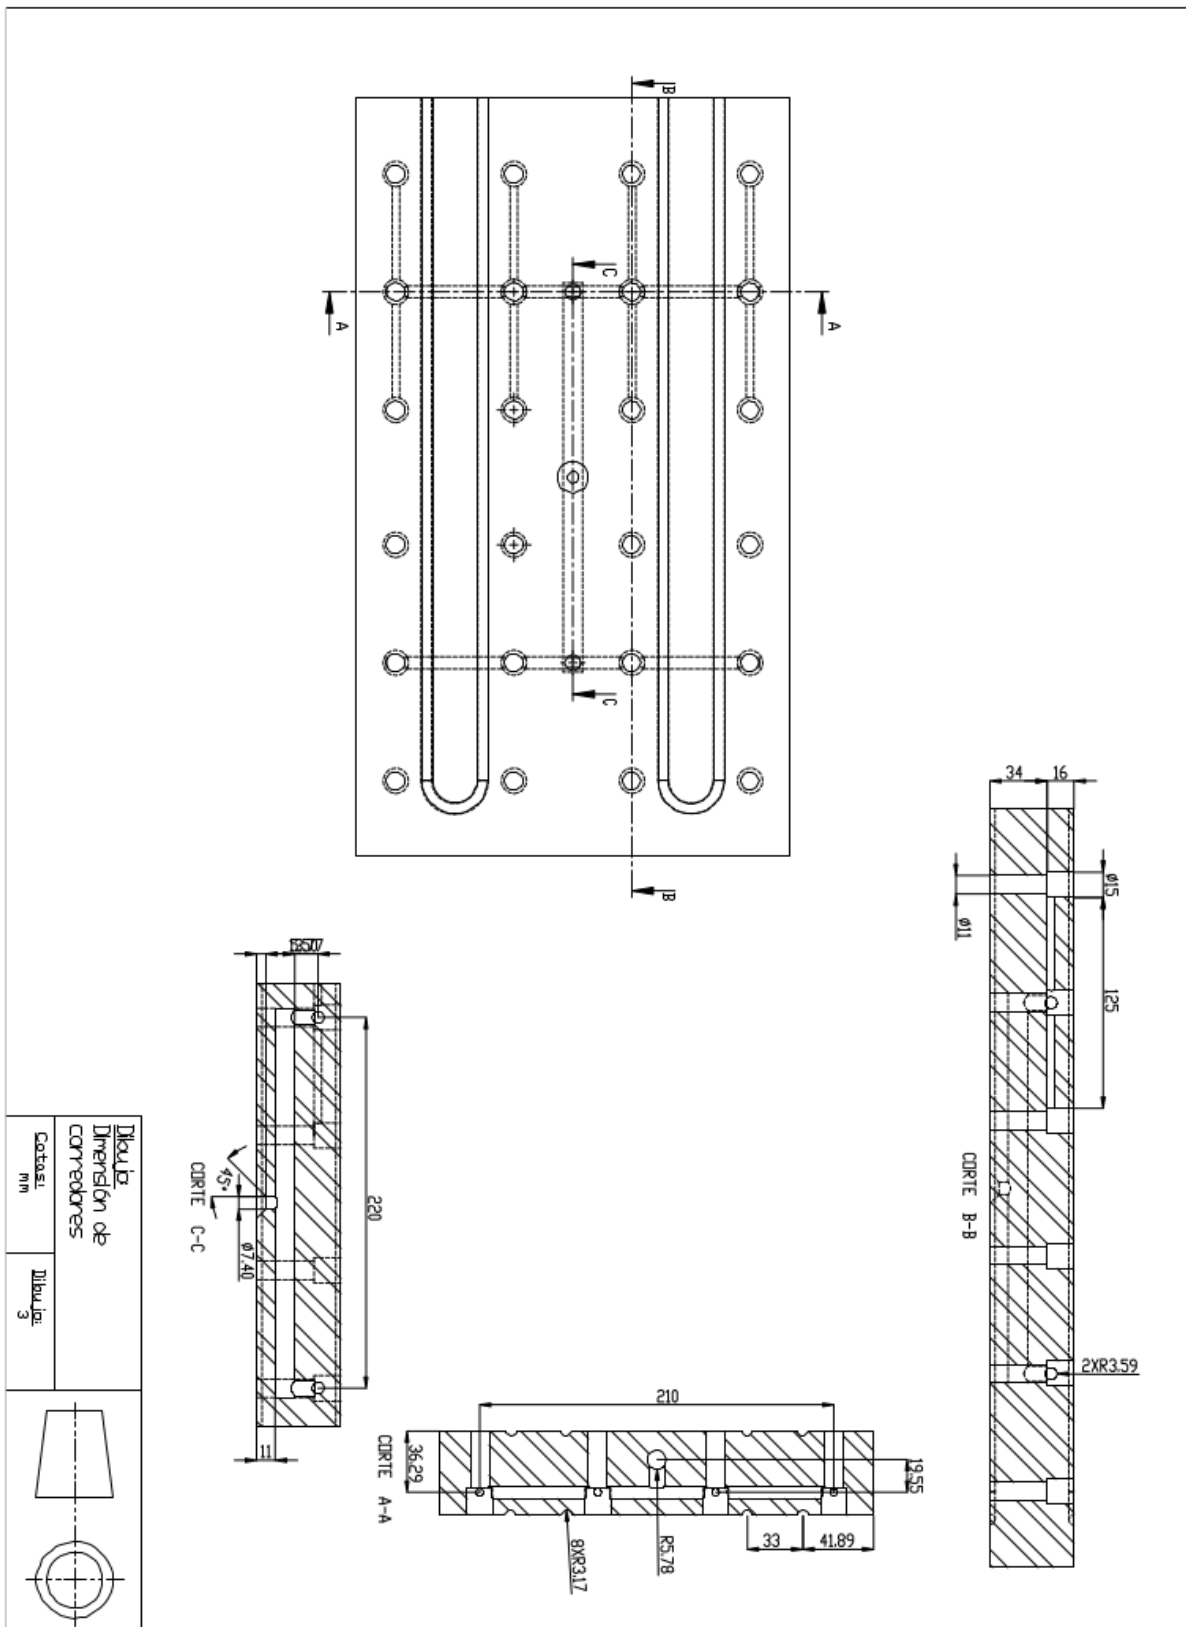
Secciones A-A, B-B, C-C del sistema de inyección
